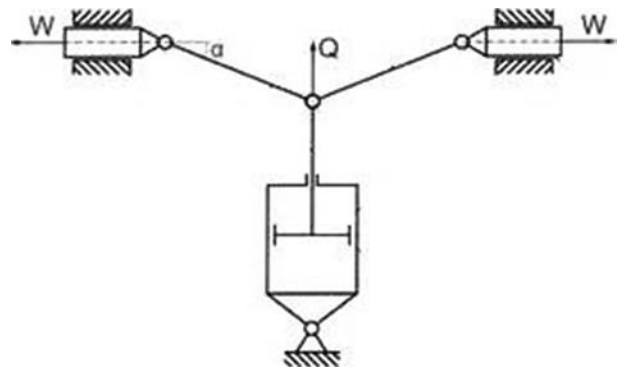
Схема устройства с рычажно-шарнирным механизмом
